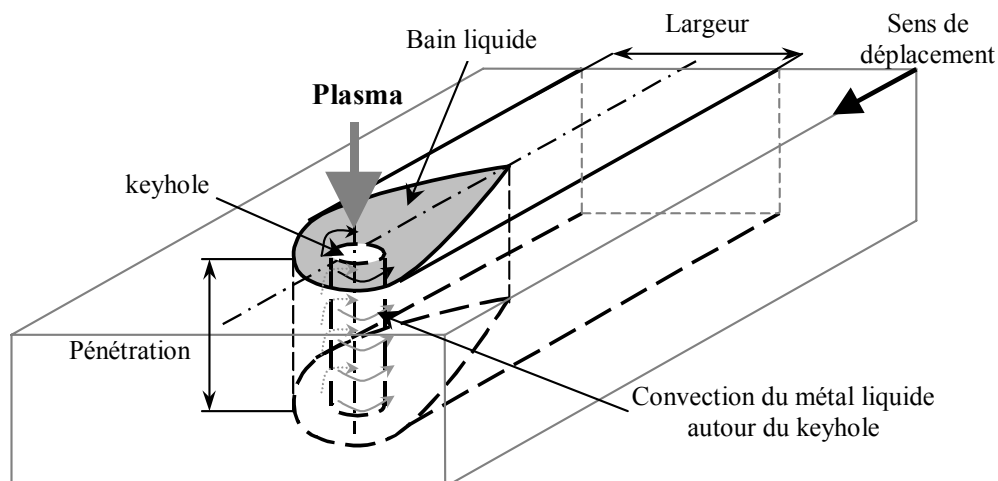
Vue schématique du keyhole en soudage plasma
